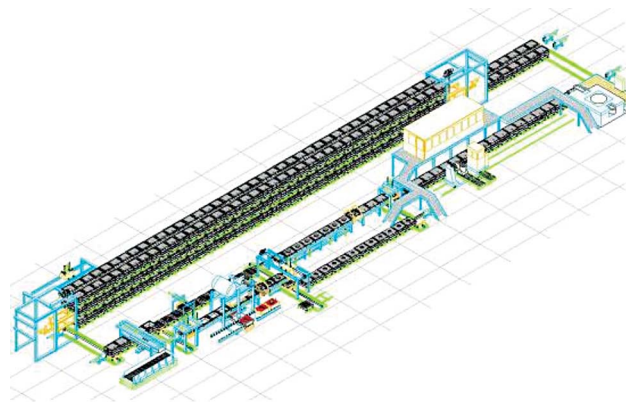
Планировка второй формовочной линии HWS-Sinto на Rexroth Guss AG (многоярусный охладитель форм)
